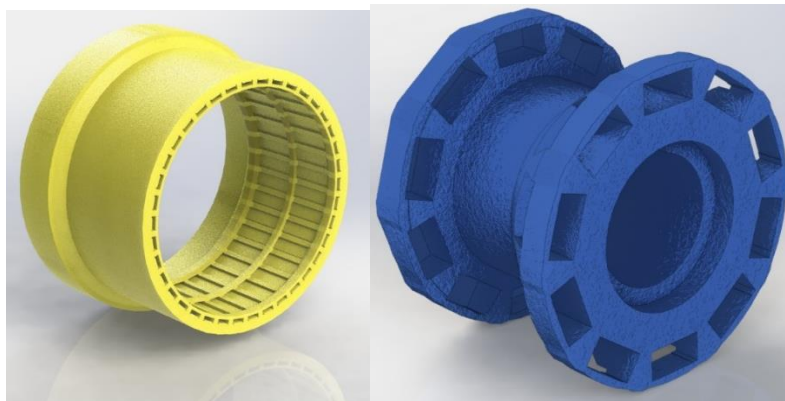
Деталі, які виготовляються методами точіння та фрезерування
